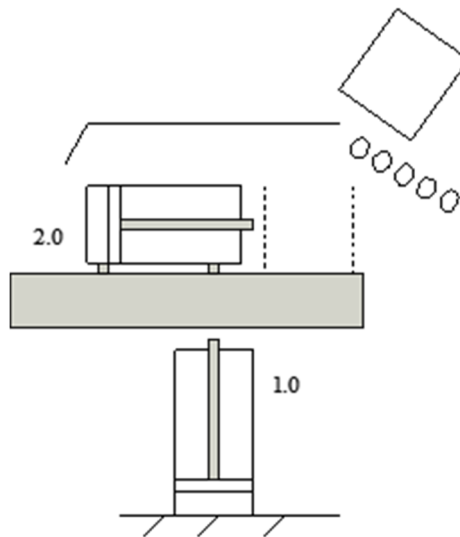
Plano de situación del sistema de elevación y posicionamiento
